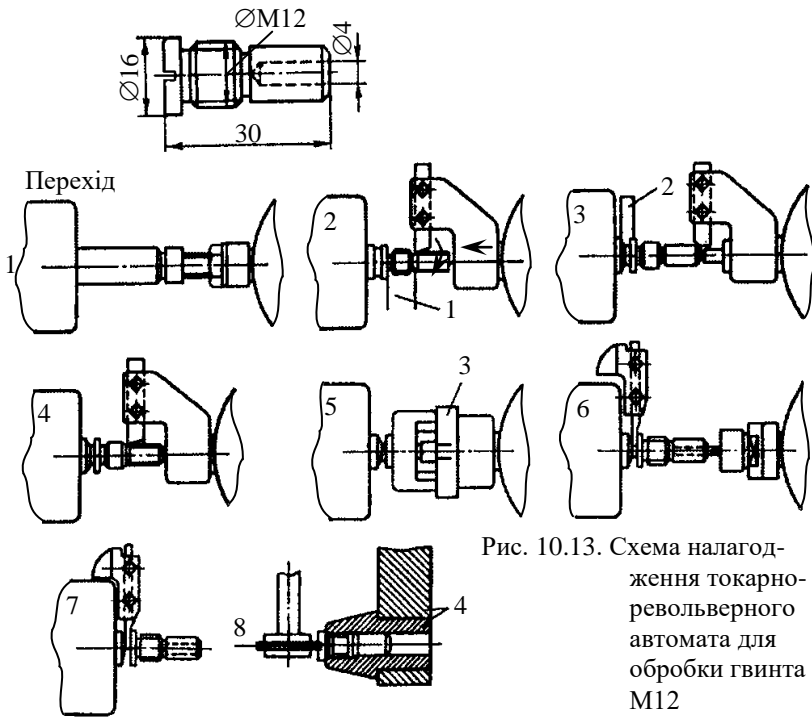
Схема налагодження токарно-револьверного автомата для обробки гвинта M12
